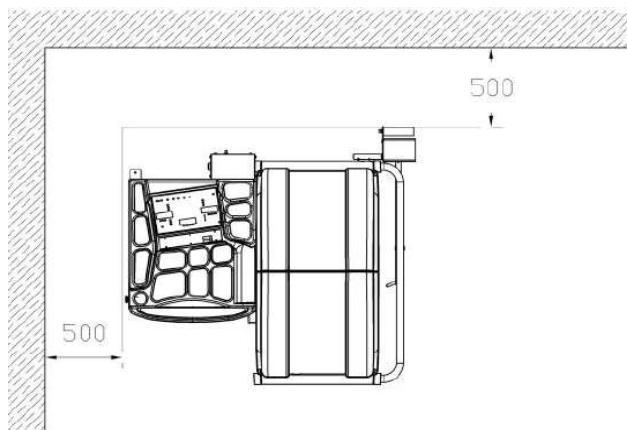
Local de instalação para máquina de balanceamento de rodas
